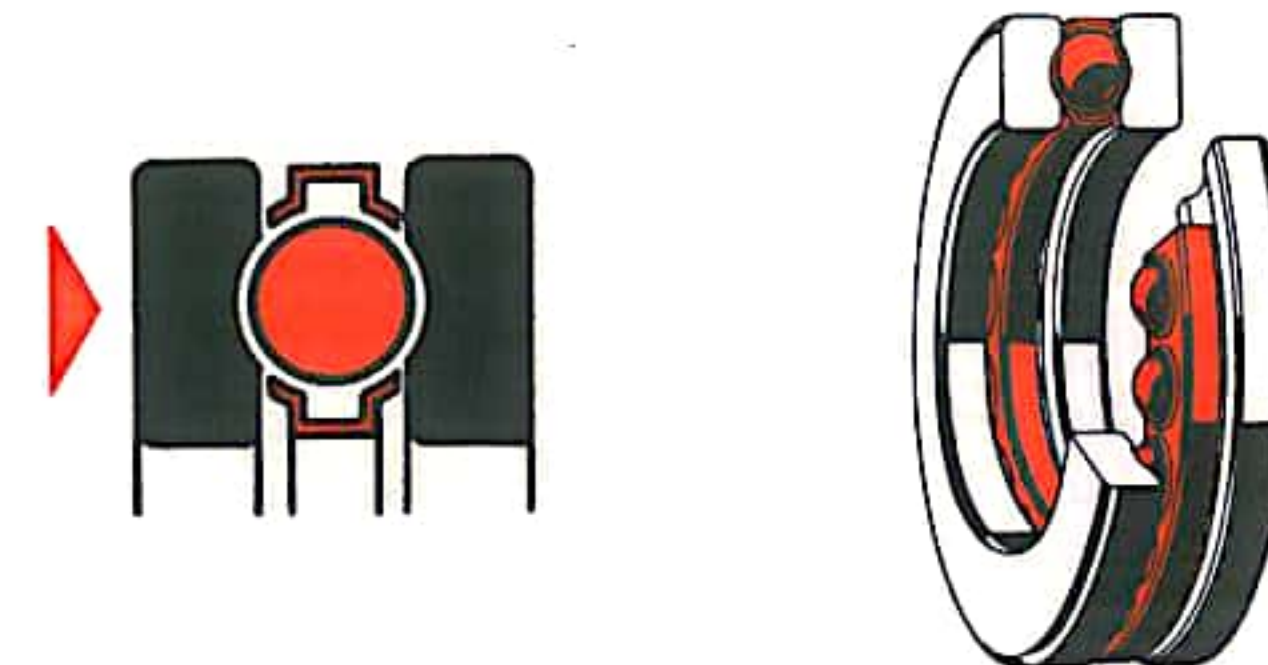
Einseitig wirkendes Axial-Rillenkugellager
